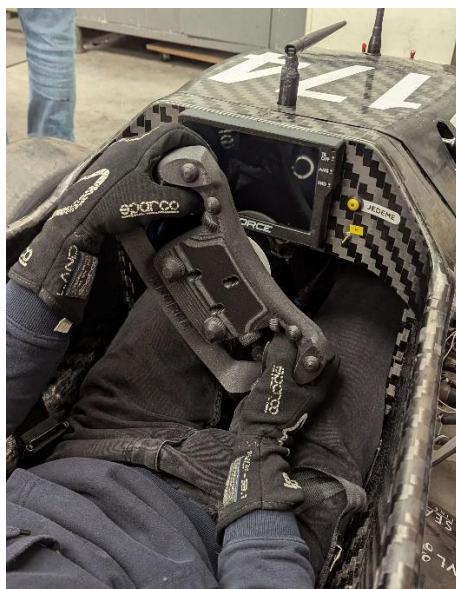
Vytištěná verze 7 s gripy oblepenými lemovou páskou a osazená dalšími testovacími přípravky
